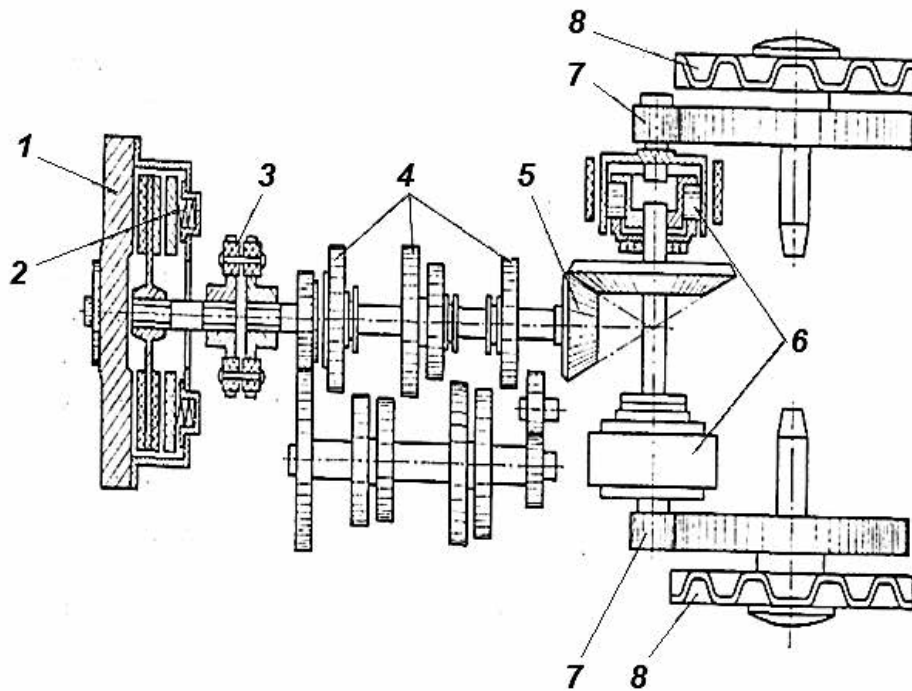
Розташування проміжного з'єднання на мобільній машині:
